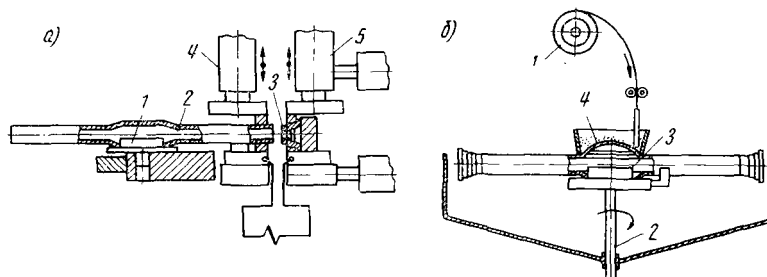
Сварка фланцев и колпака балки заднего моста автомобиля «Москвич» модели 407
